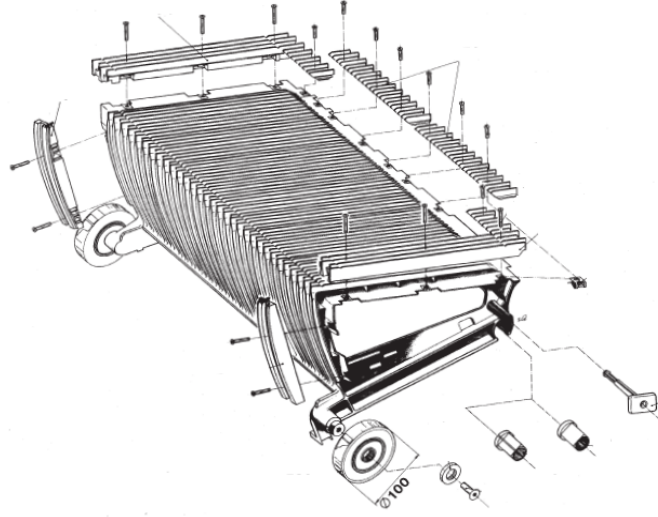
Basamak bağlantı mili montaj parçaları
